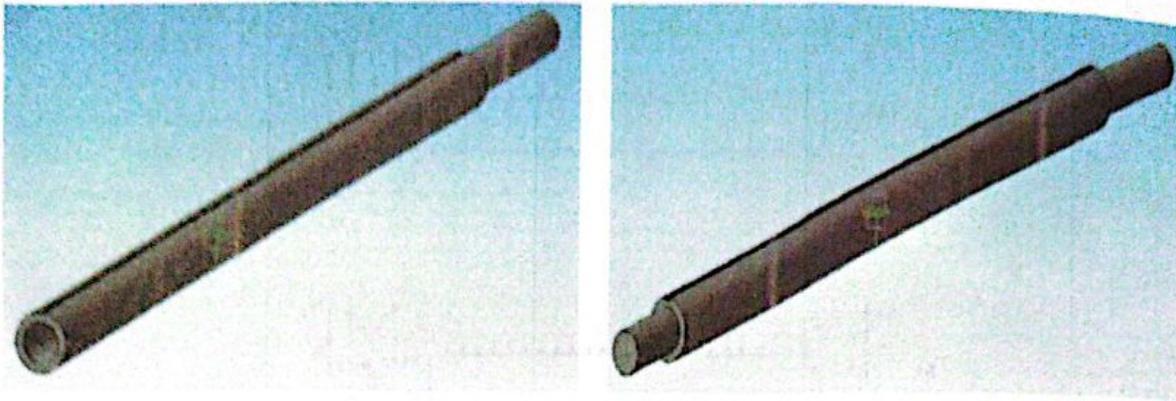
3D-модель предлагаемой конструкции полого вала
